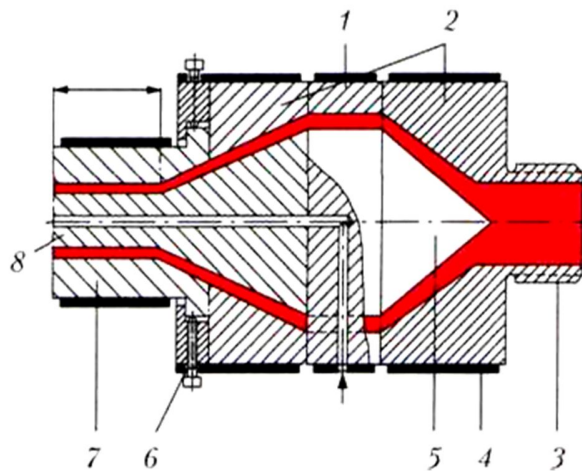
Екструзійна головка для виробництва труб: 1- тримач дорна; 2- корпус; 3- кріплення; 4- нагрівач; 5- наконечник дорна; 6- центруючий елемент; 7-фільєра; 8- дорн.
